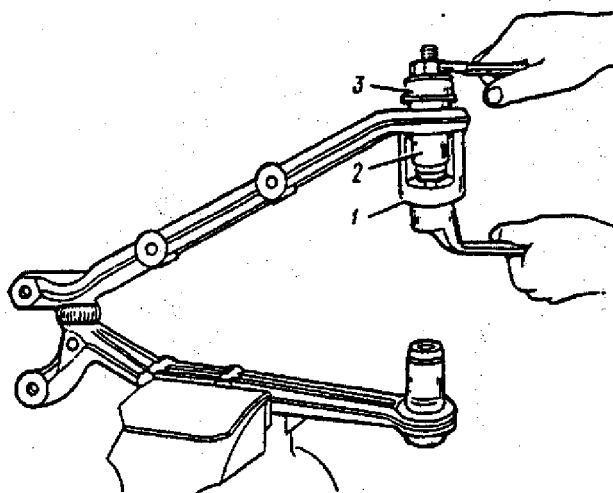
Instalação da bucha isolante do braço inferior: 1 - dispositivo 67.7823-9517; 2 - bucha isoladora; 3 - apoio.
